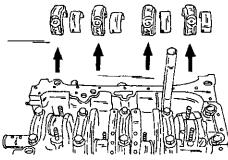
После маркировки крышек подшипников и шатунов снять крышки и вкладыши подшипников.
